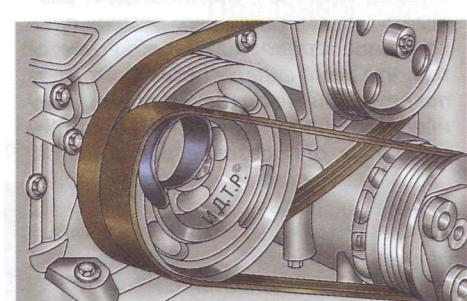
Монтаж ремня привода компрессора кондиционера на шкив коленчатого вала
